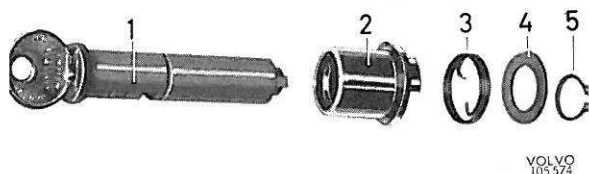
Bouton-poussoir de fermeture de porte désassemblé
